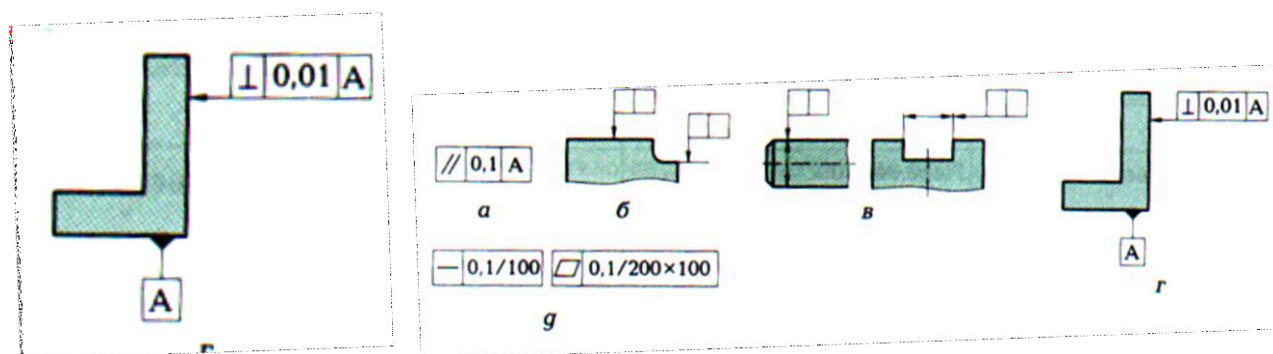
Условные обозначения допусков расположения и формы на чертежах:
